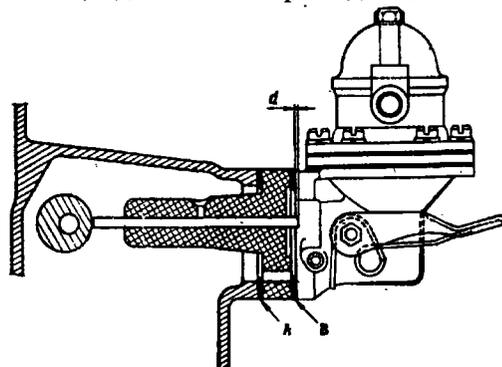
Схема для контроля и регулировки выступа толкателя привода насоса: А - прокладка толщиной 0,27-0,33 мм; В - прокладка толщиной 0,70-0,80 мм; d - выступание толкателя
